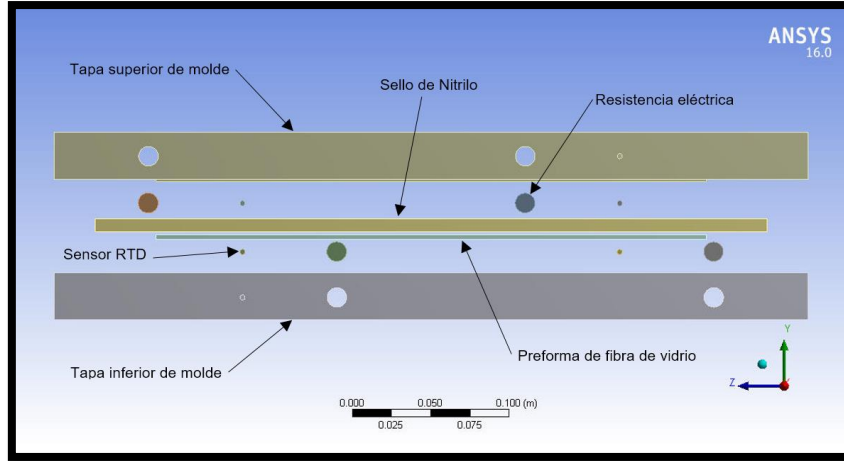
Vista frontal con proyecciones de elementos de molde para espécimen.
